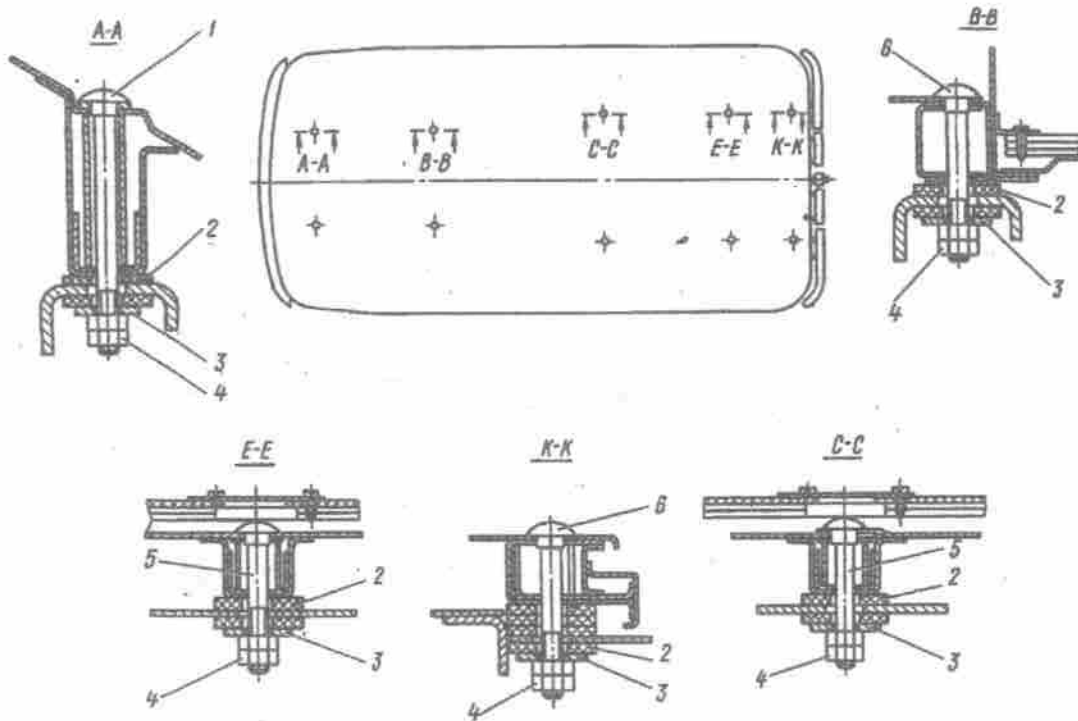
Befestigung der Karosserie und der Führerkabine am Rahmen:
